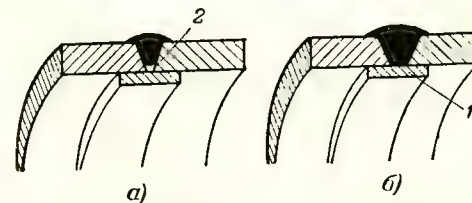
Неправильная (а) и правильная (б) формы сварного шва при стыковой сварке труб большого диаметра.
